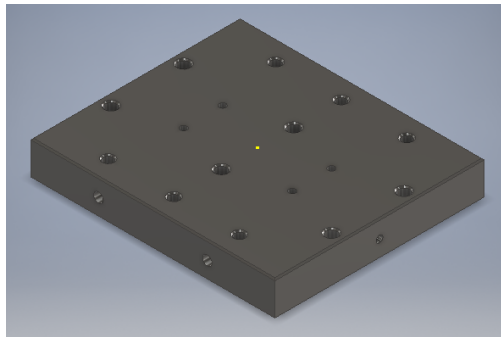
Placas auxiliar para refrigerar el macho de moldeo.
